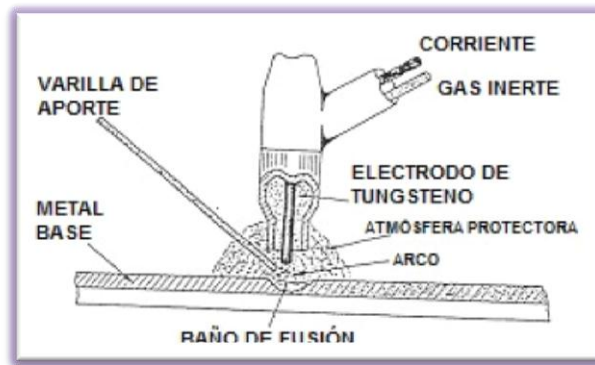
Proceso de Soldadura TIG (2)
